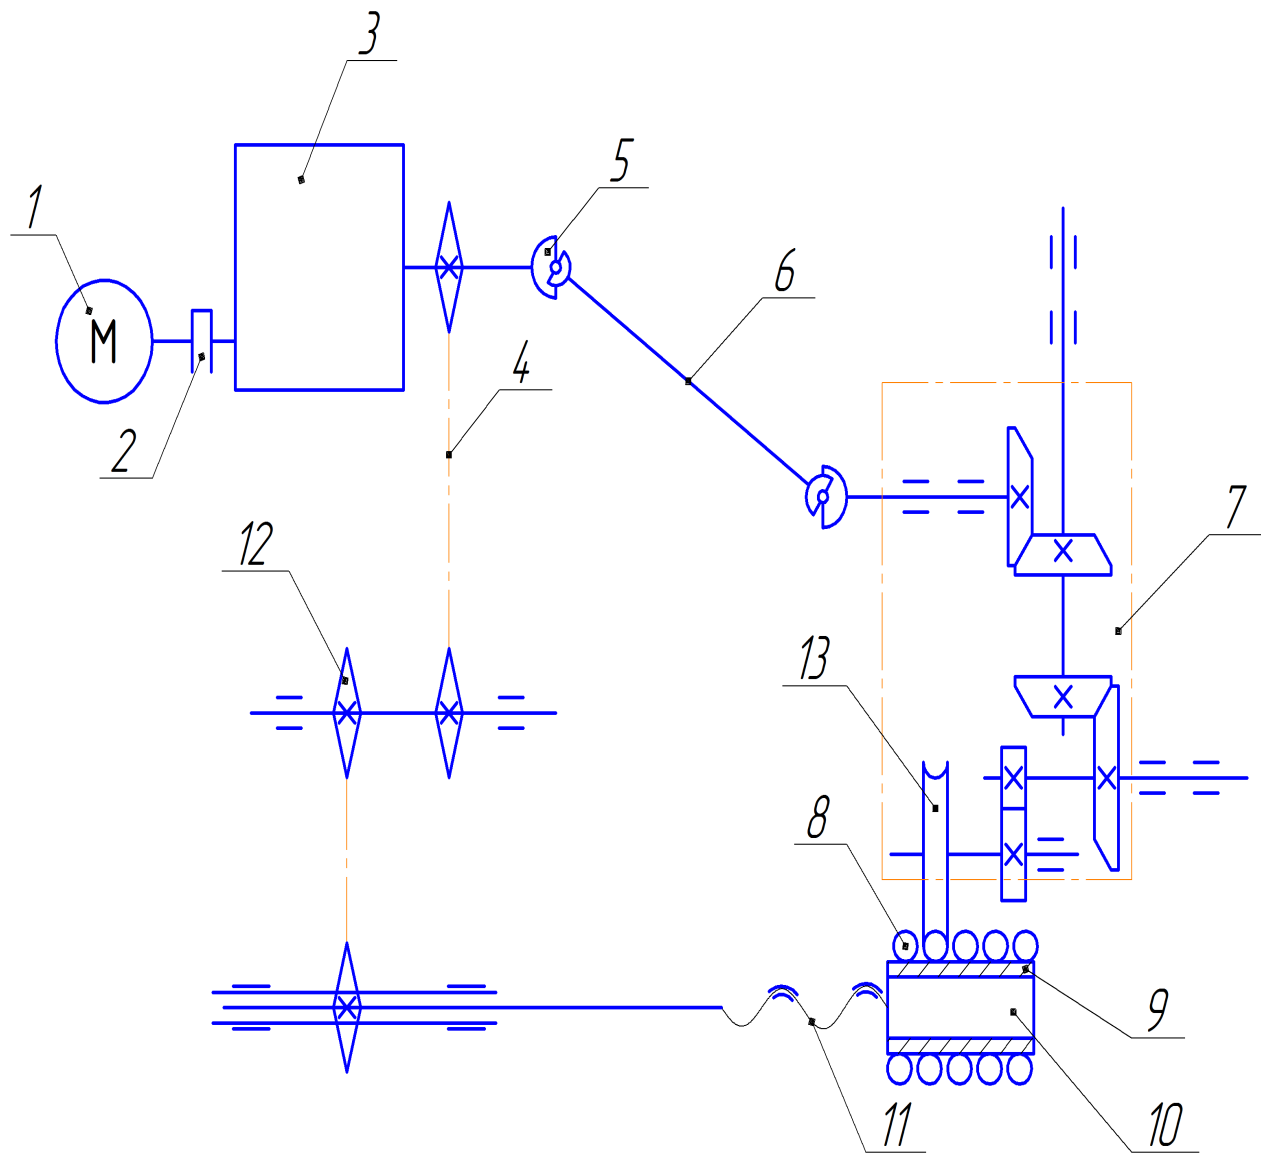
Кинематическая схема машины МШ – 2001 – 1 после модернизации: 1-Электродвигатель; 2-Муфта; 3-Редуктор; 4-Цепная передача; 5-Кардан; 6-Вал; 7-Редуктор; 8-Электрод; 9-Заготовка; 10-Цанговый патрон; 11-Винт; 12-Цепная передача; 13-Дисковый электрод.
